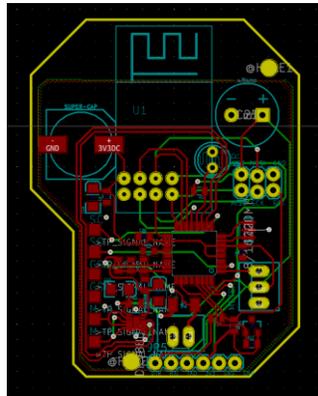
Vista PCB de la nueva versión del dispositivo para agua y gas
